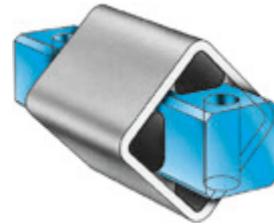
Innenvierkant aus Vollmaterial mit zwei Bohrungen
